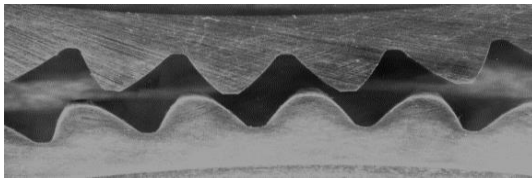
Фрагменти зубчастих коліс до і після термоімпульсної обробки
